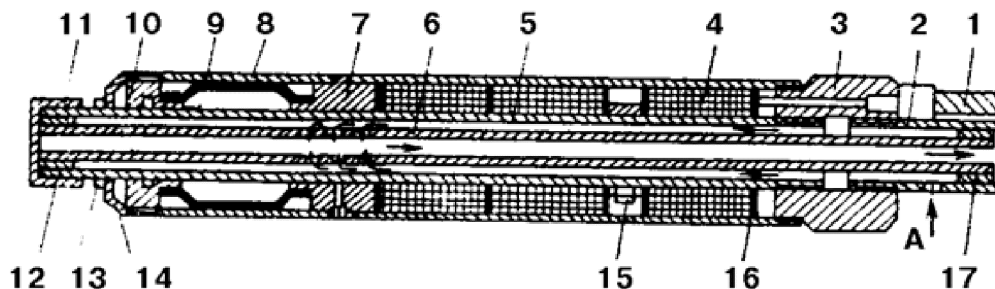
Нагреватель электрический скважинный индукционный НЭСИ50-122М:
